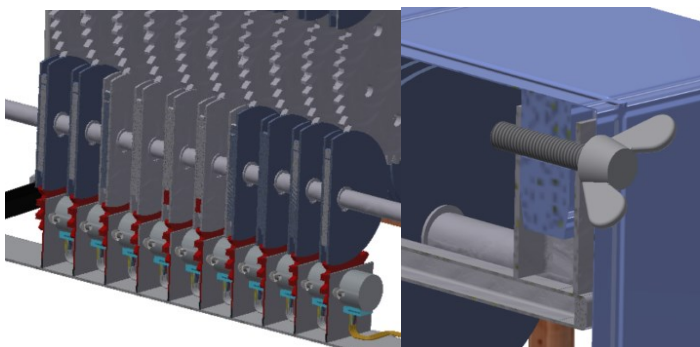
Detail A – zobrazení pružiny, Detail B/C – zobrazení pohonu navíječe [Vlastní tvorba]
